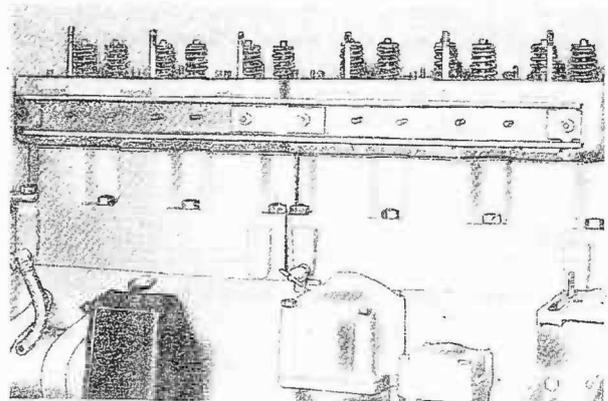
Ausrichten der Zylinderköpfe mittels Richtleiste
